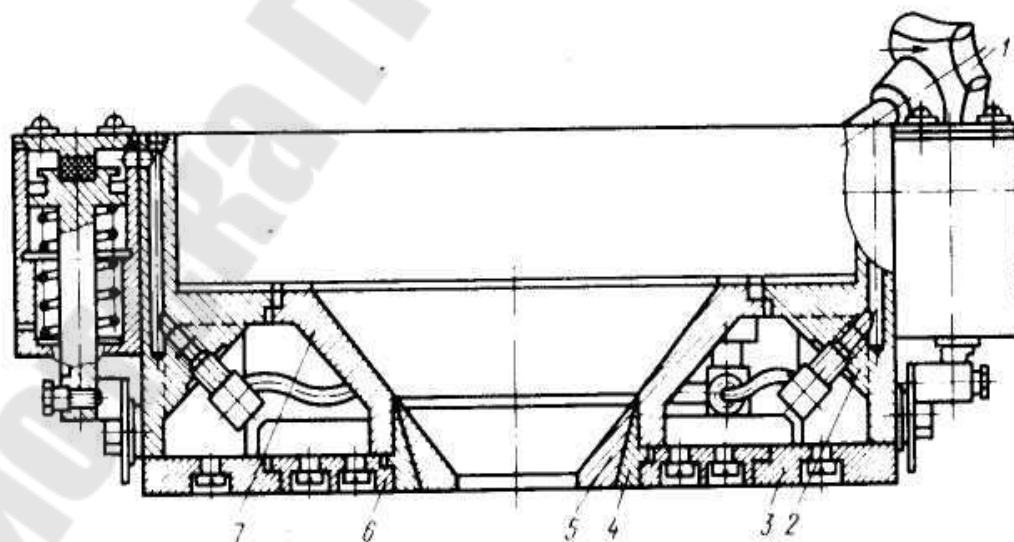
Устройство насадки пескодувного резервуара полуавтомата мод.2Б83
